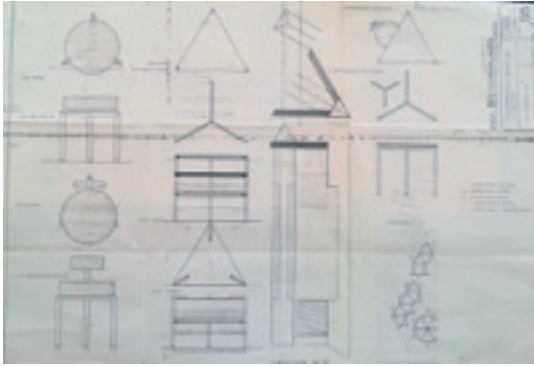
Plano de planta y sección de taburetes, sillas y mesas diseñadas como un mecano.
